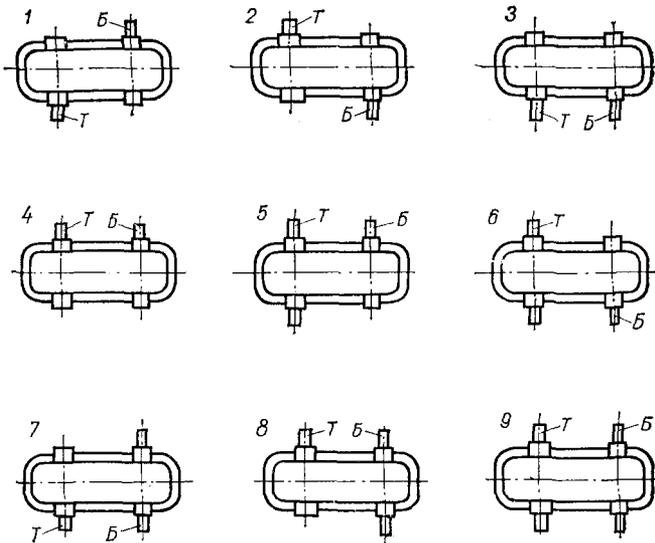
Схемы сборок (1—9) редукторов ЦОН:
